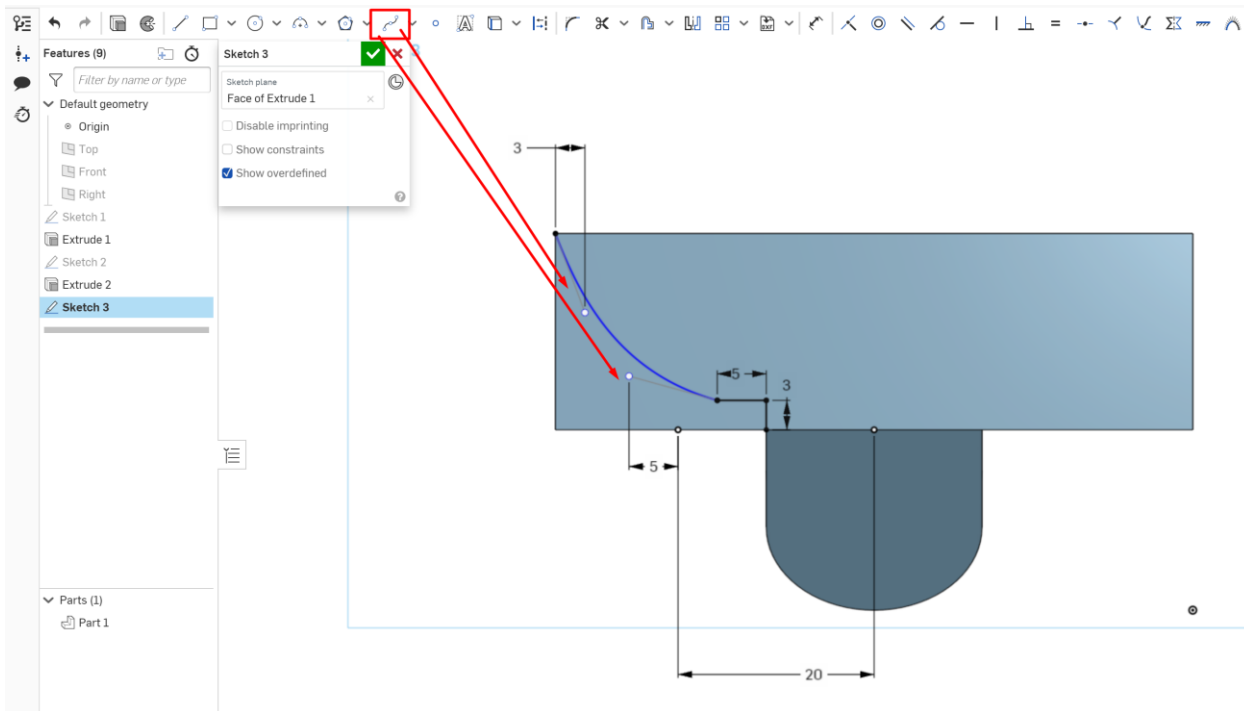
Формування робочого контуру верхньої частини з одного боку
